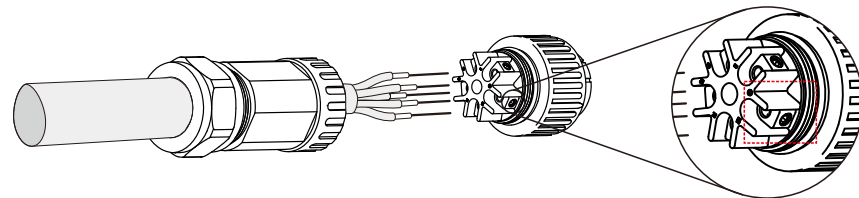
Konstrukcja wewnętrzna złącza prądu
